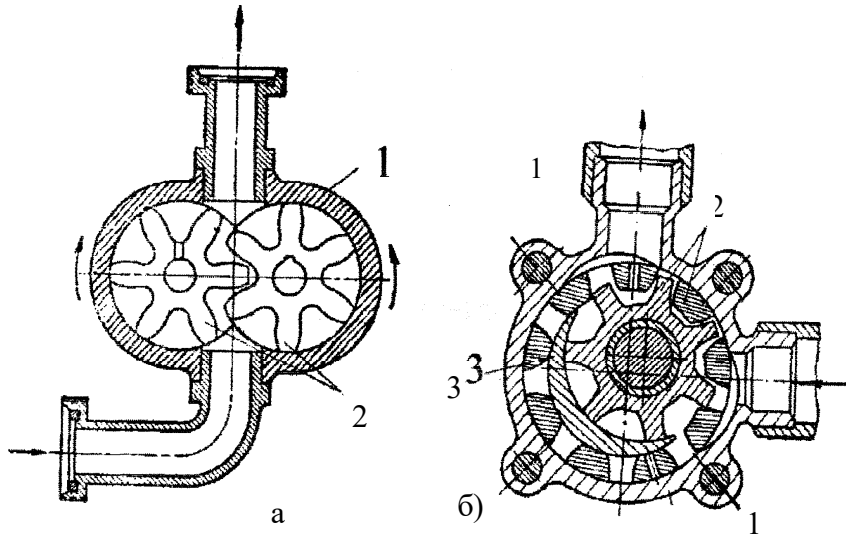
Схема шестеренних насосів: а – із зовнішнім зчепленням; б – з внутрішнім зчепленням; 1 – корпус; 2 – шестерні; 3 – виступ в корпусі.
